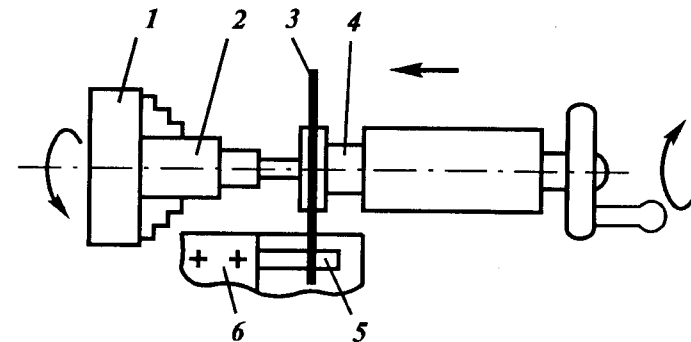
Нарезание резьбы плашкой на токарно-винторезном станке: 1 — трехкулачковый патрон; 2 — заготовка; 3 — плашкодержатель с плашкой; 4 — пиноль задней бабки; 5 — планка; 6 — резцедержатель
